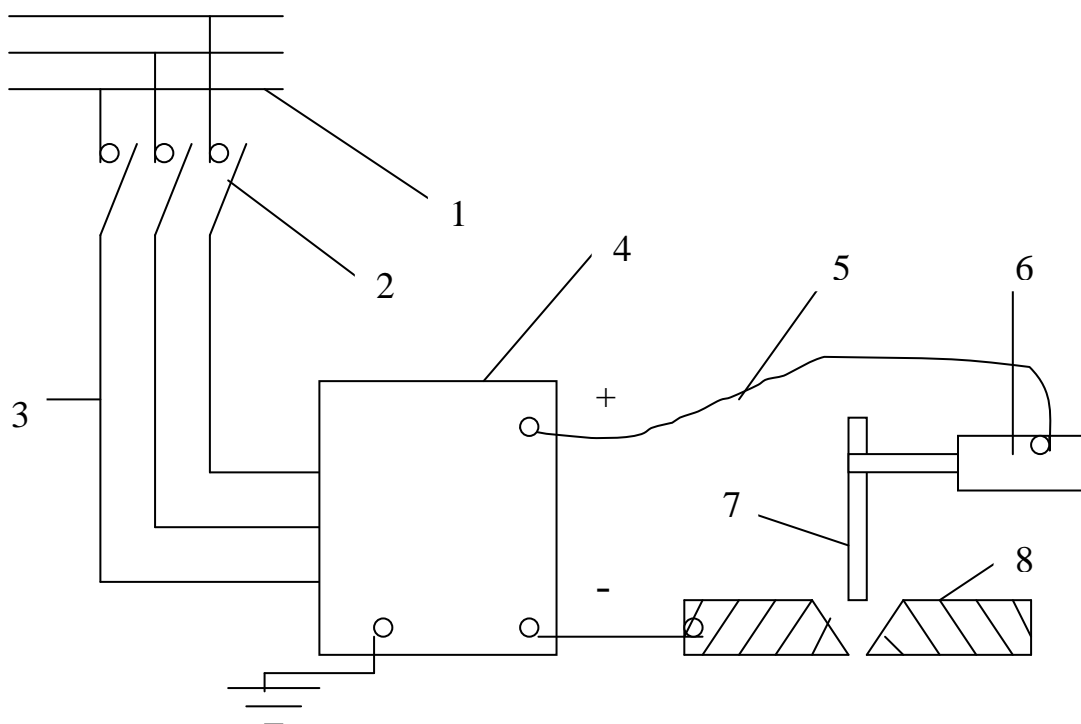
Схема посту для ручного дугового зварювання на постійному струмі від зварювального випрямляча: 1 – трьохфазна електрична мережа з напругою 380 В; 2 – рубильник; 3 – електричні проводи; 4 – зварювальний випрямляч; 5 – зварювальні проводи; 6 – електродотримач; 7 – зварювальний електрод; 8 – виріб, що зварюється.
